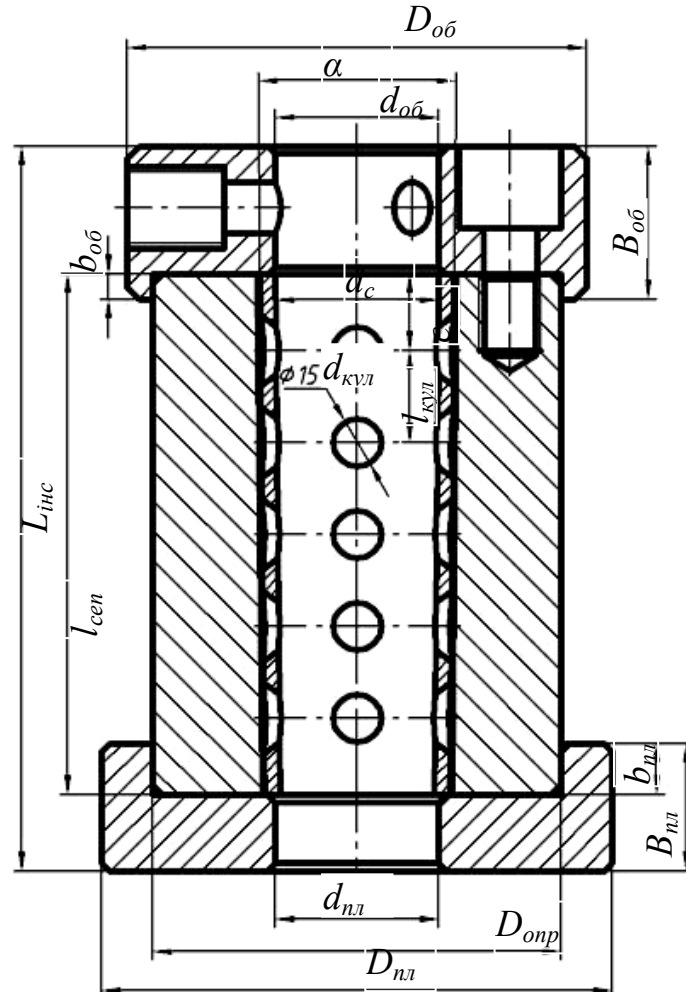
Розрахункова схема для визначення конструктивних параметрів інструменту для калібрування зовнішніх напівкруглих шліцьових канавок
